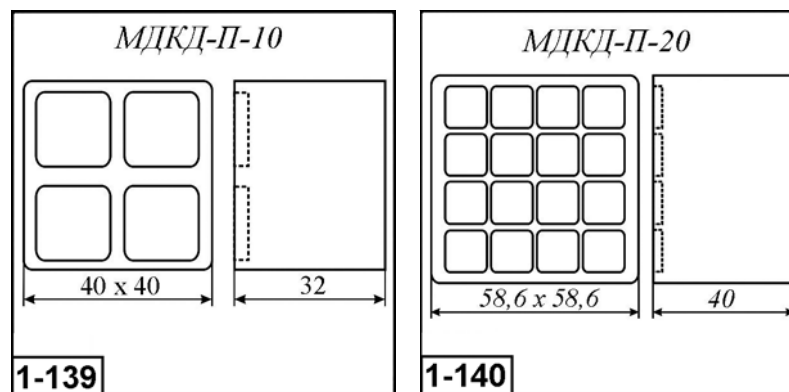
Внешний вид и габаритные размеры детекторов типа МДКП-П.
